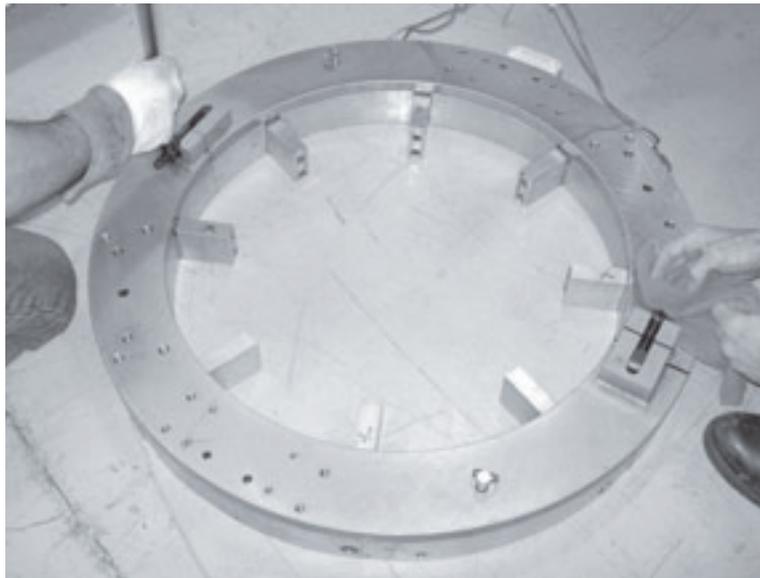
Assemblare la macchina a terra per l'utilizzo su un tubo aperto.
